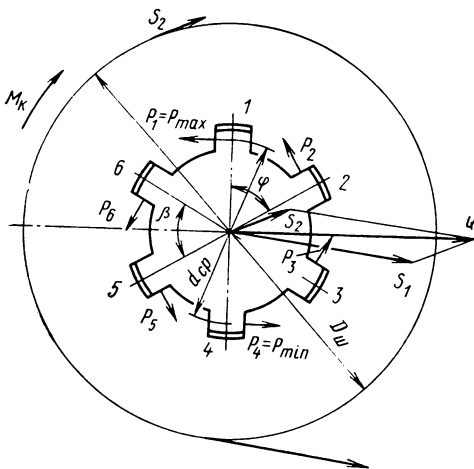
Схема нагружения шлицевого соединения вала со шкивом ременной передачи
